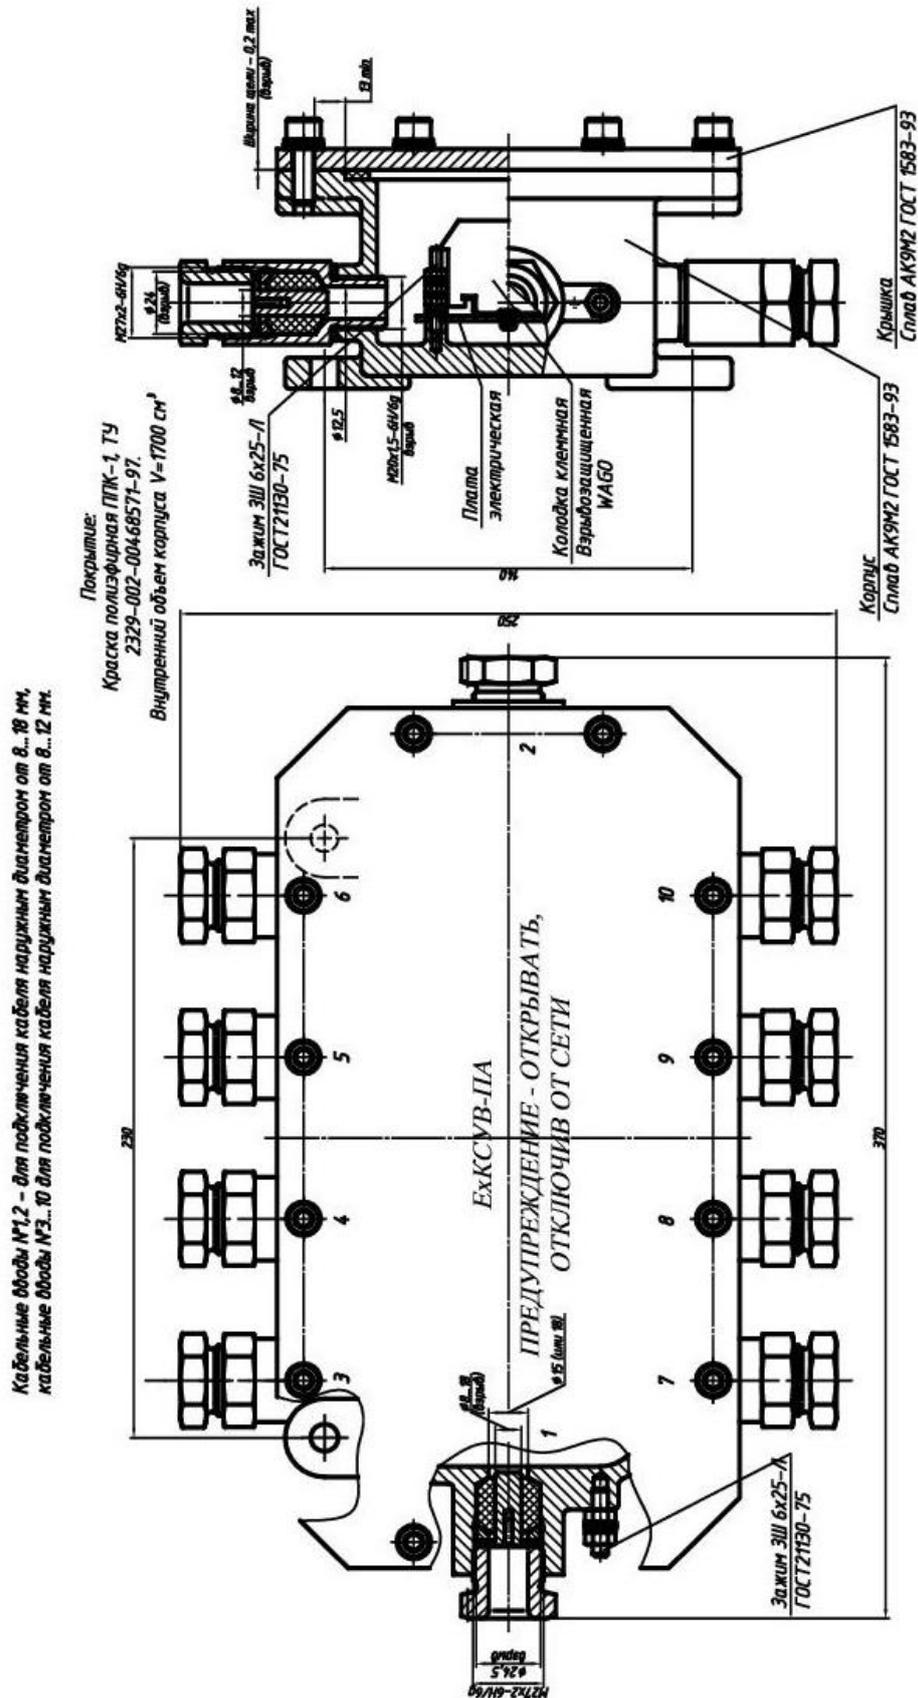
Габаритный чертеж коробки ЕхКСУВ-ПА, совмещённый с чертежом взрывозащиты
